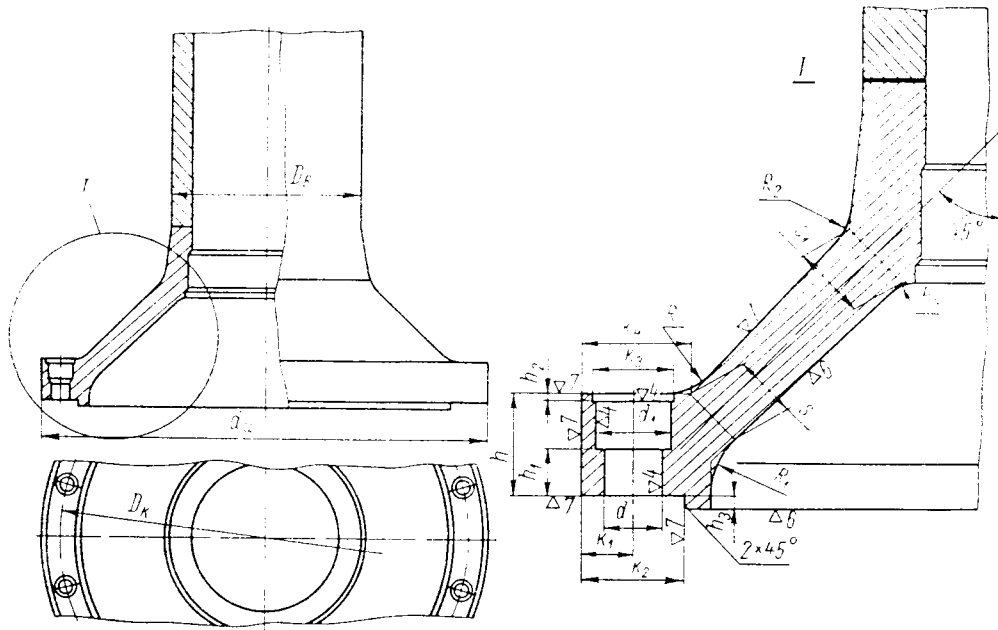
Вал турбины, объединенный с крышкой рабочего колеса
